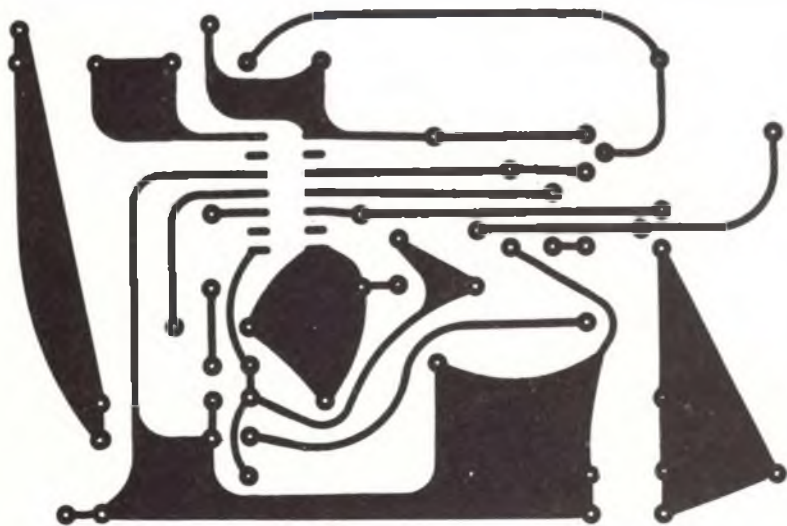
Disegno del circuito stampato dell'alimentatore duale in scala 1 : 1.
